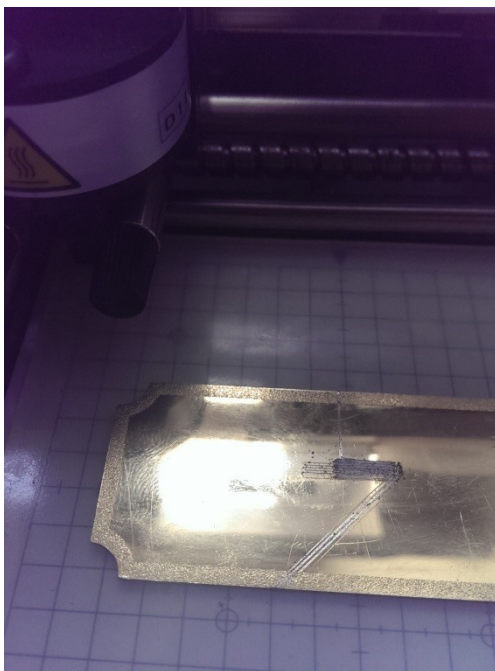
Глубокие царапины на поверхности заготовки из тонкой и «мягкой» заготовки из латуни
